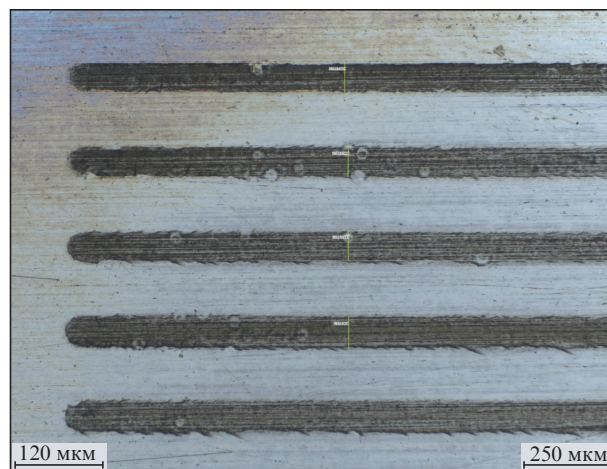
Внешний вид сварных швов сверху, соединение нержавеющая сталь–стекло.
